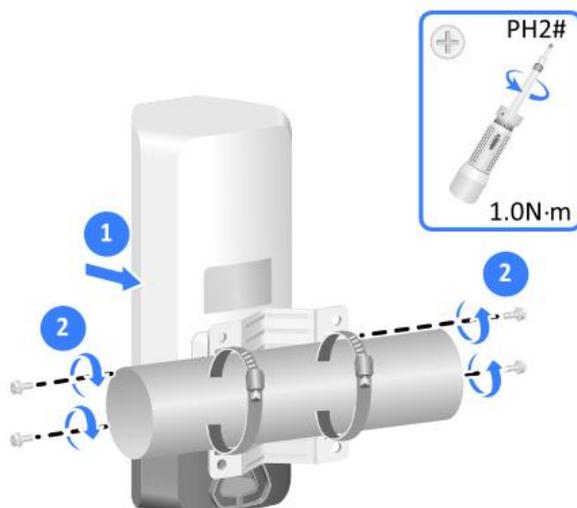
Asegure el Dispositivo al Soporte de Montaje
